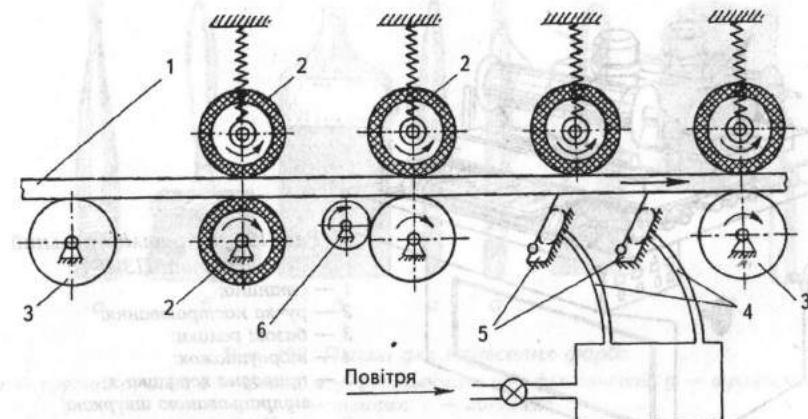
Схема роботи вальцювального верстата для втирання порозаповнювача:
